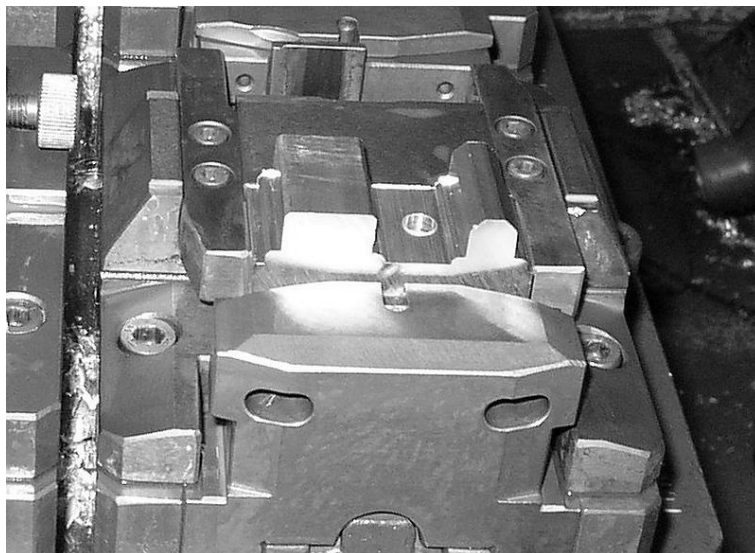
Po obrobení boční roviny obrobku 1. upnutí
